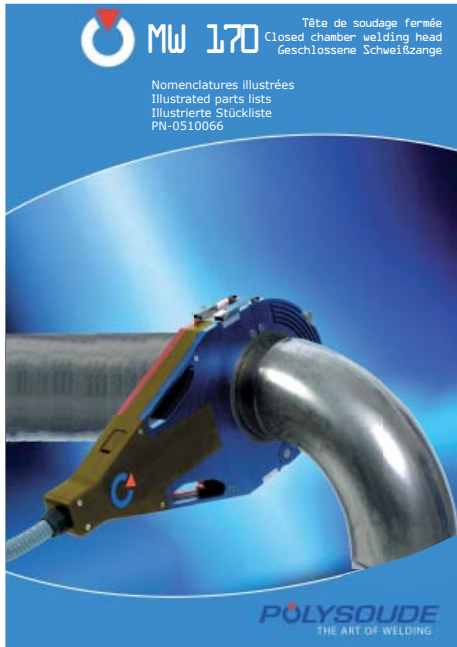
Illustrierte Stücklisten der MW-Schweißzangen
